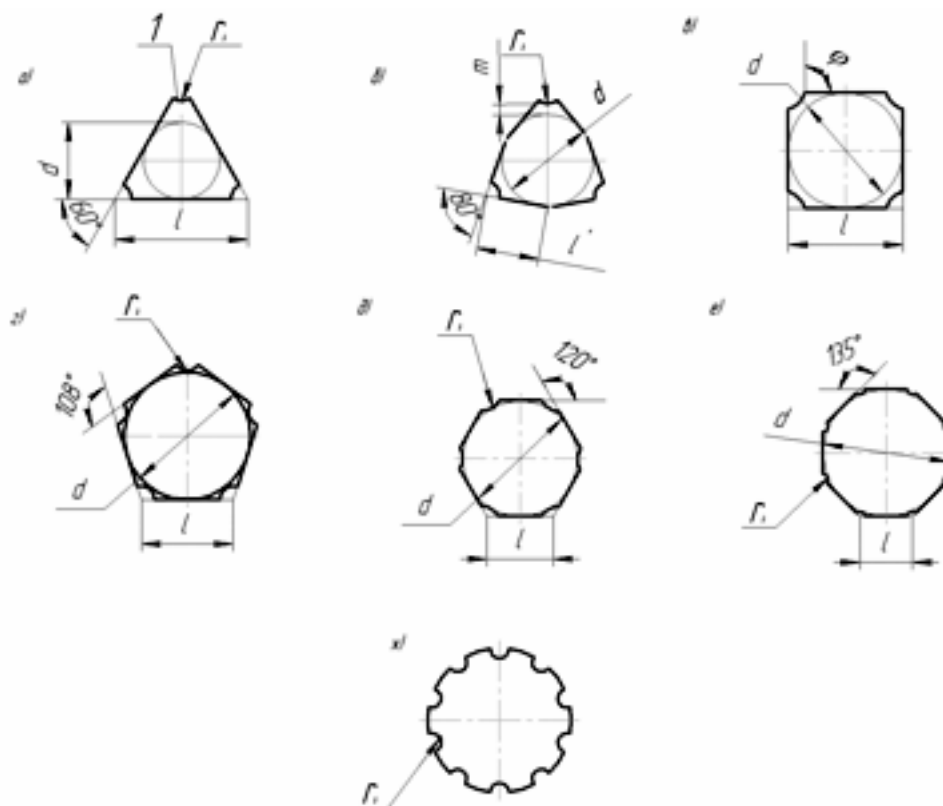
Предлагаемые варианты исполнения МНП без отверстий с дуговыми выкружками-стружечными канавками на боковых сторонах у вершин режущих кромок
